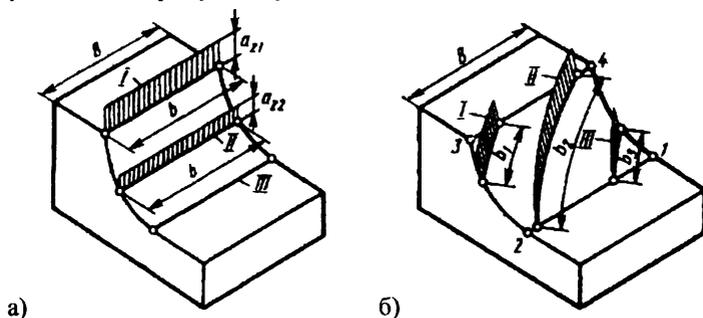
Параметры сечения среза при обработке цилиндрической фрезой с прямыми (а) и винтовыми (б) зубьями
